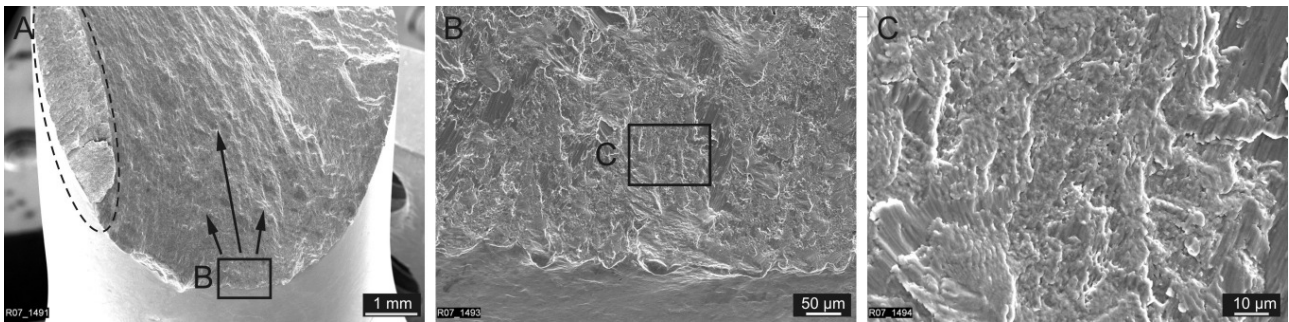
Rissausgang Ausschnitt B aus Bruchfläche Detail C, Mikroduktilität
